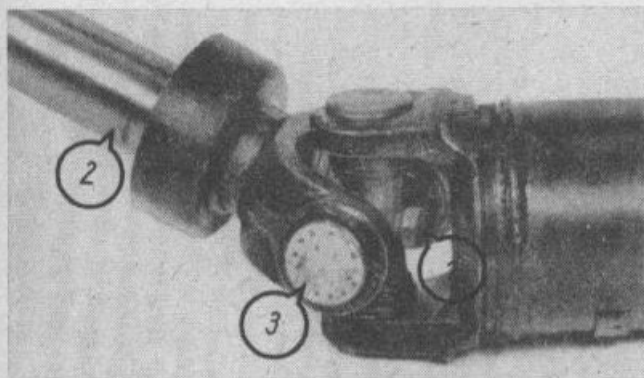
Gelenkwelle des Moskwitsch 412/2140 mit vorderem Kreuzgelenk und Schiebestück; 1 – Verschußschraube, 2 – Schiebestück, 3 – Abdeckkappe für Nadellager
